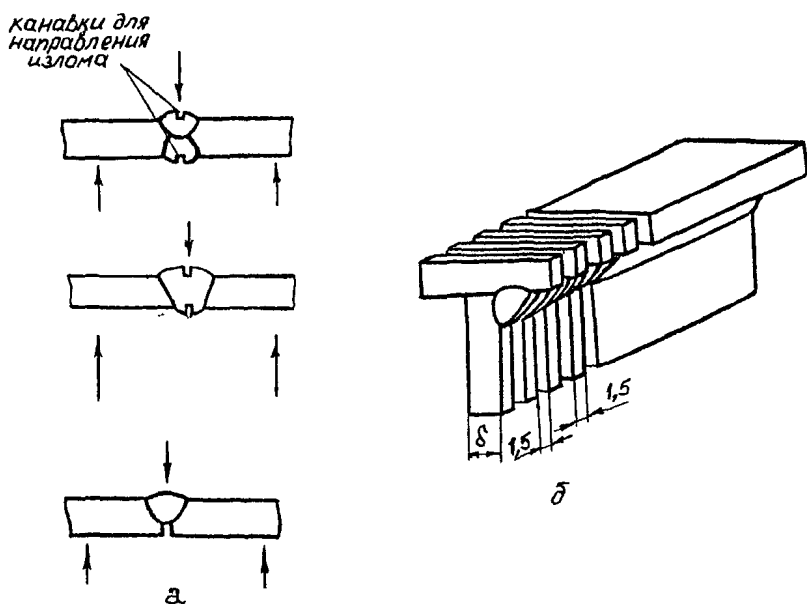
Вскрытие сварных швов изломом (а)
